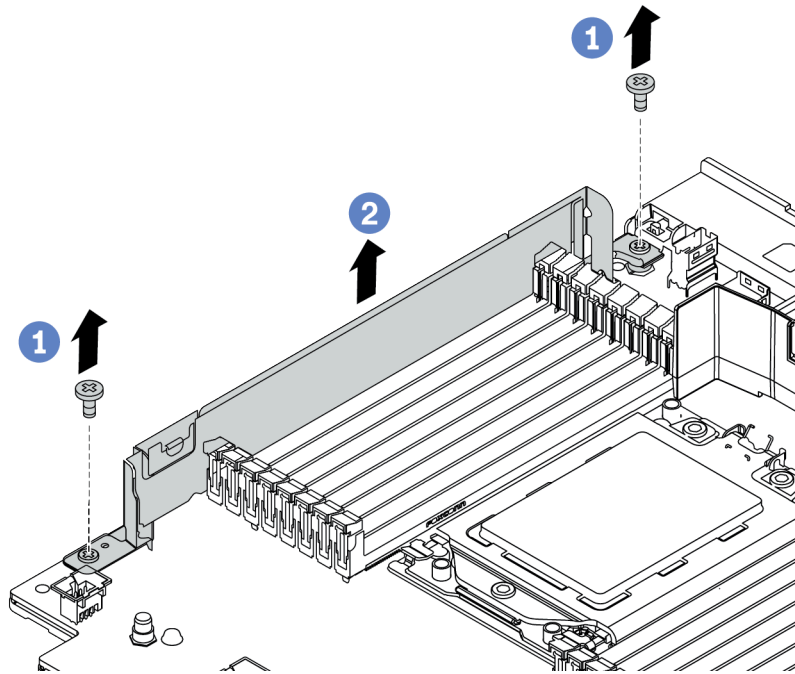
Rimozione della staffa per il montaggio a parete con cavo
